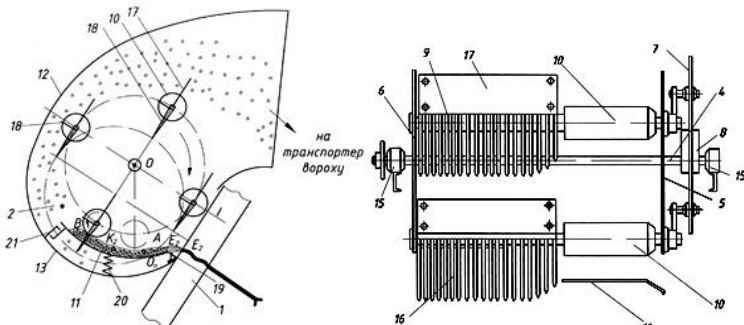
Плющильно-обчисувальний апарат: 1 – затискний транспортер; 2 – обчисувальна камера; 3 – барабан; 4 – вал; 5, 6, 7 – диски; 8 – ексцентриковий механізм; 9 – гребені; 10 – плющильні вальці; 11 – опорна направляюча поверхня; 12 – корпус; 13 – піддон; 14, 15 – підшипники; 16 – обчисувальні зуби; 17, 18 – лопаті; 19 – куліса; 20 – пружина; 21 – упор
